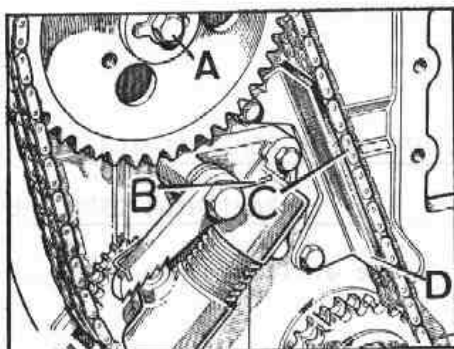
J Montaje tensor hidráulico, patín y fijación engranaje árbol de levas
